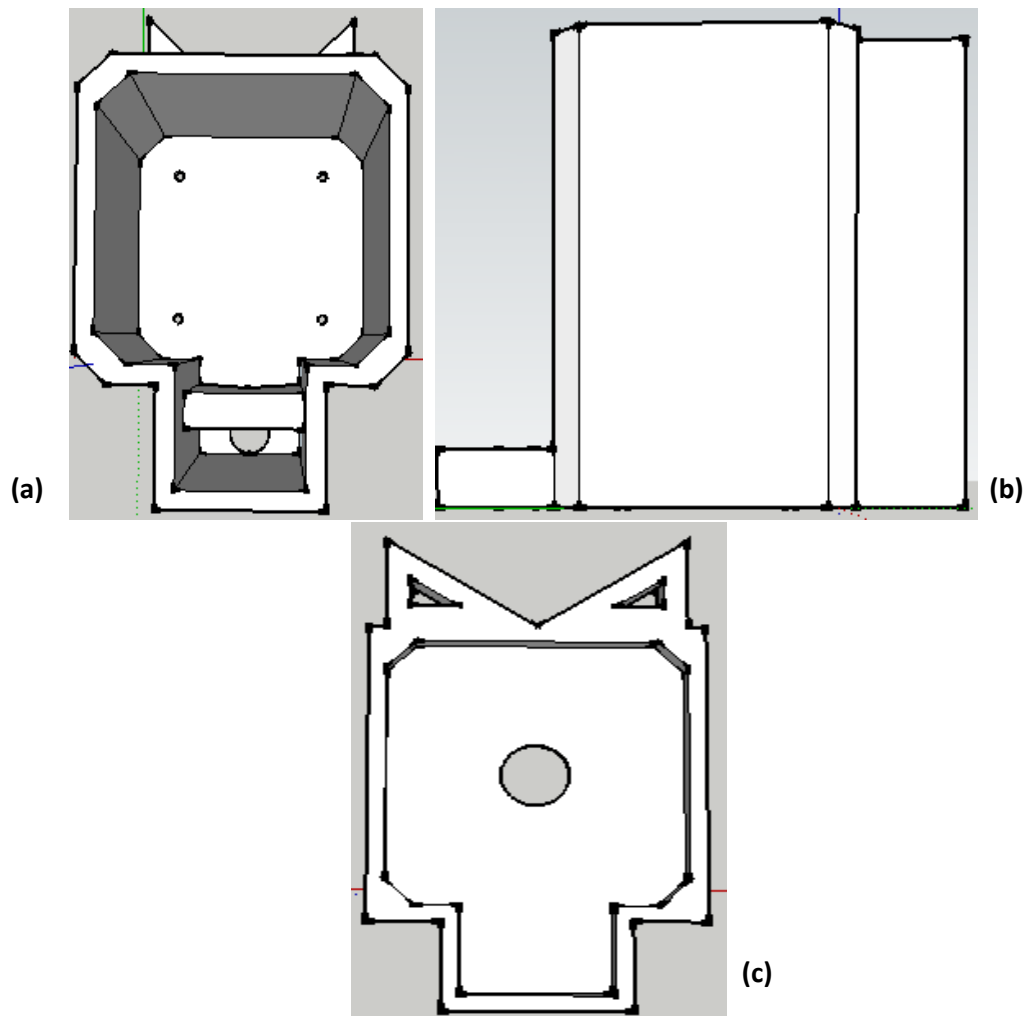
Caixa estanque para proteção do motor de passo: (a) visto do topo, (b) vista de perfil, (c) tampa da caixa.
